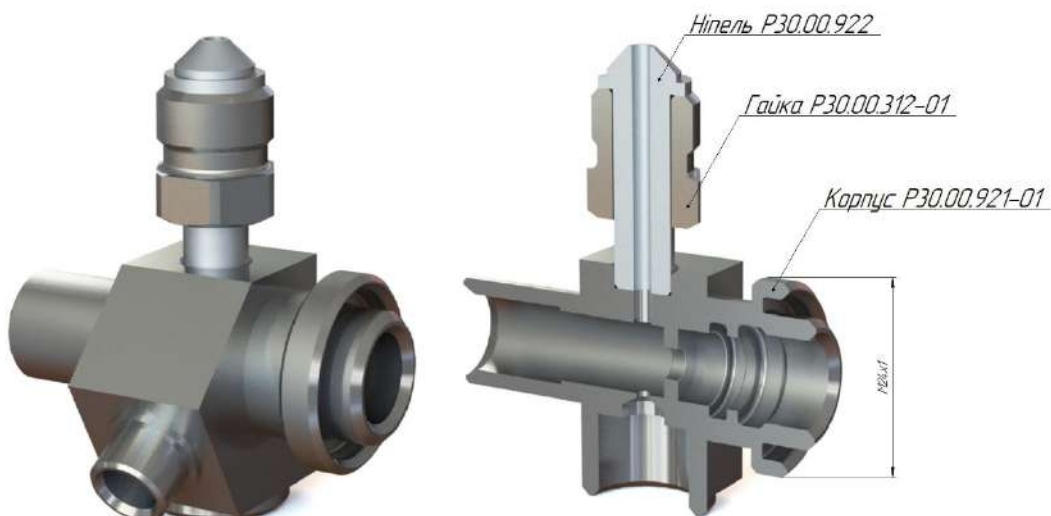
Конструктивні варіанти корпусу сигнального пристрою в залежності від типу заготовки
